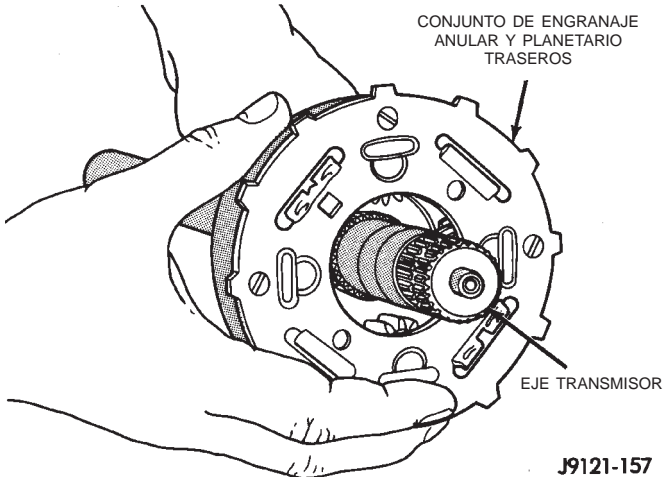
Ensamblaje del engranaje anular y planetario trasero
